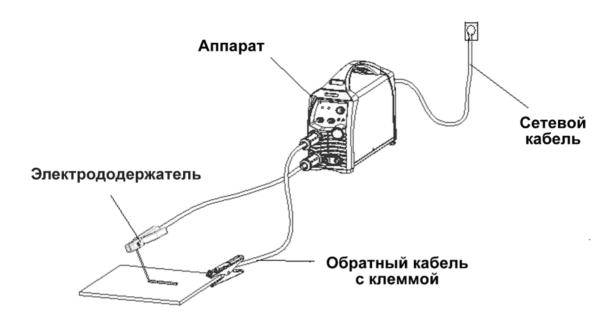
Схема подключения оборудования для ММА сварки
